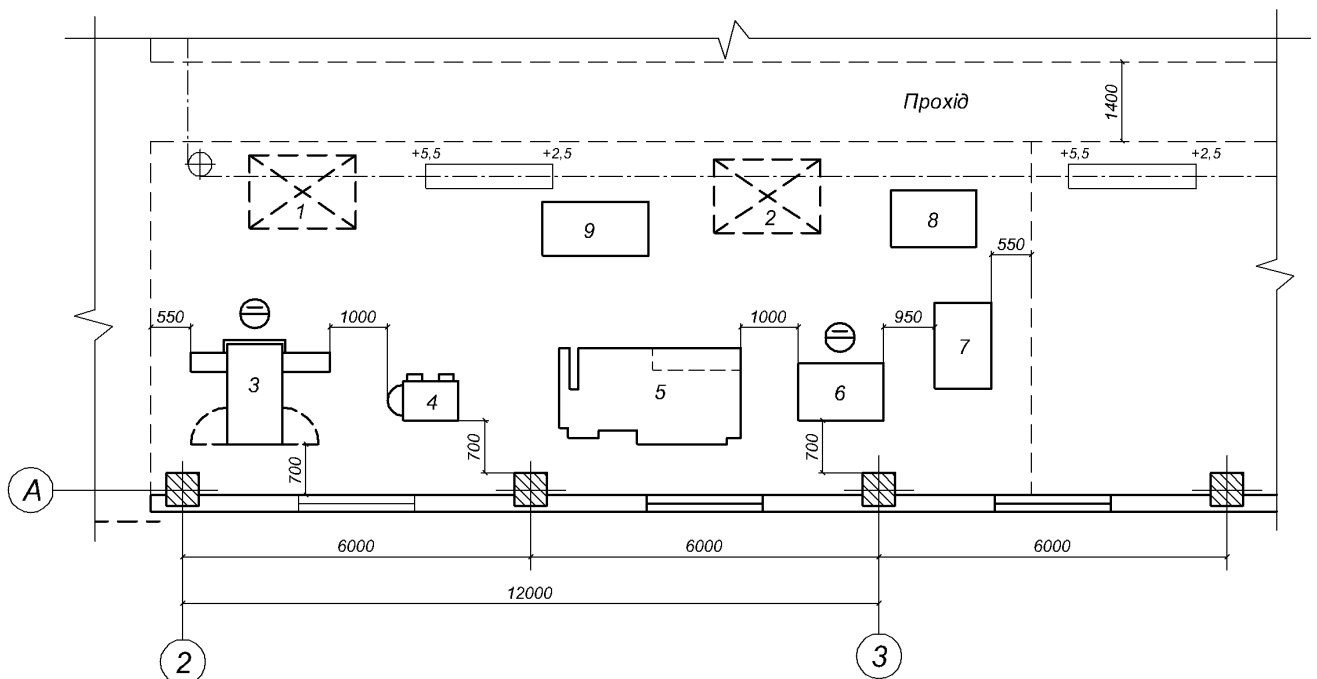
План розміщення обладнання на ділянці механічної обробки деталі «корпус ПС-10.02.024»:
